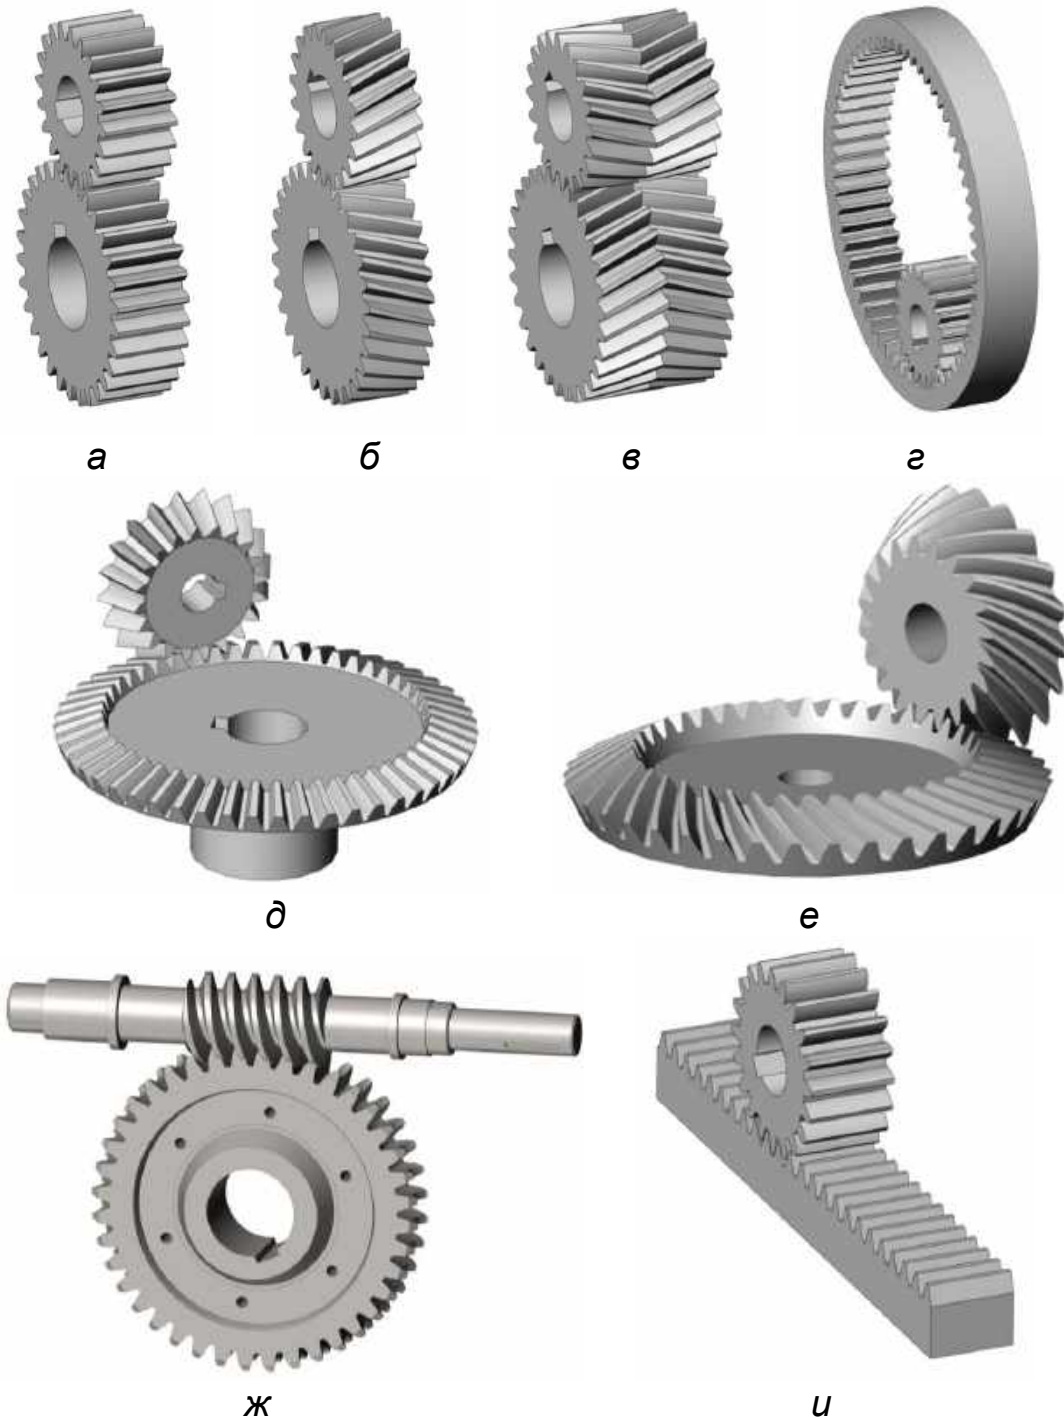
Види зубчастих передач: а–в – циліндричні зубчасті передачі із зовнішнім зачепленням; г – циліндрична передача з внутрішнім зачепленням; д, е – конічні зубчасті передачі; ж – черв'ячна передача; и – рейкова передача
